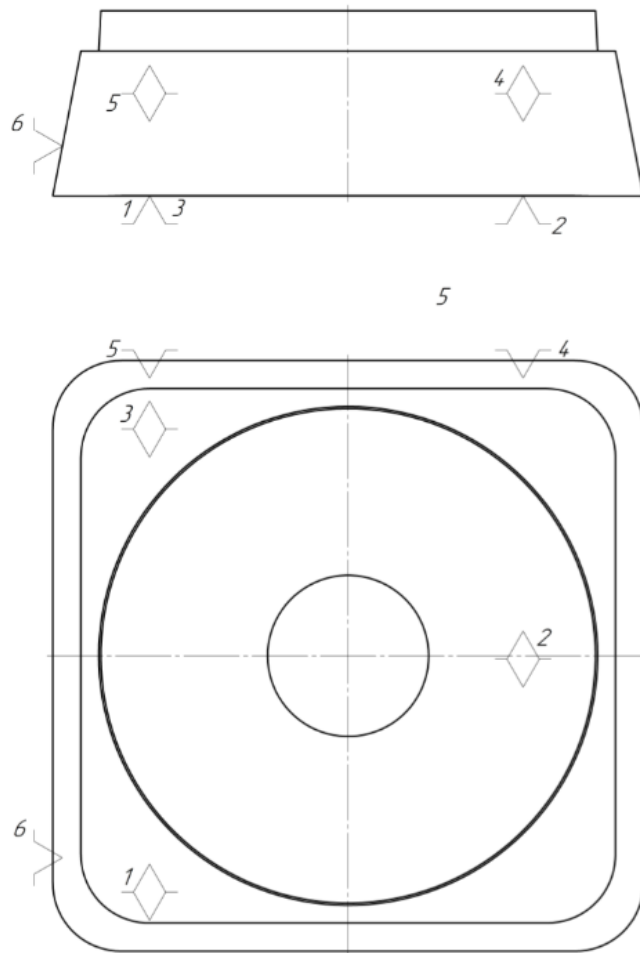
Схема базування деталі «Корпус» по ТБ 1.
